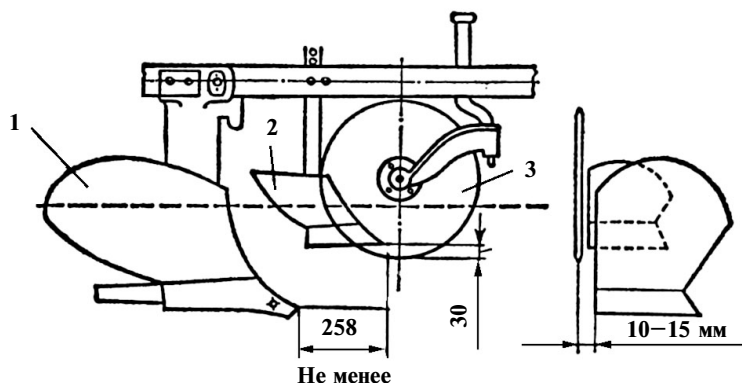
Схема для установки дискового ножа и предплужника:
